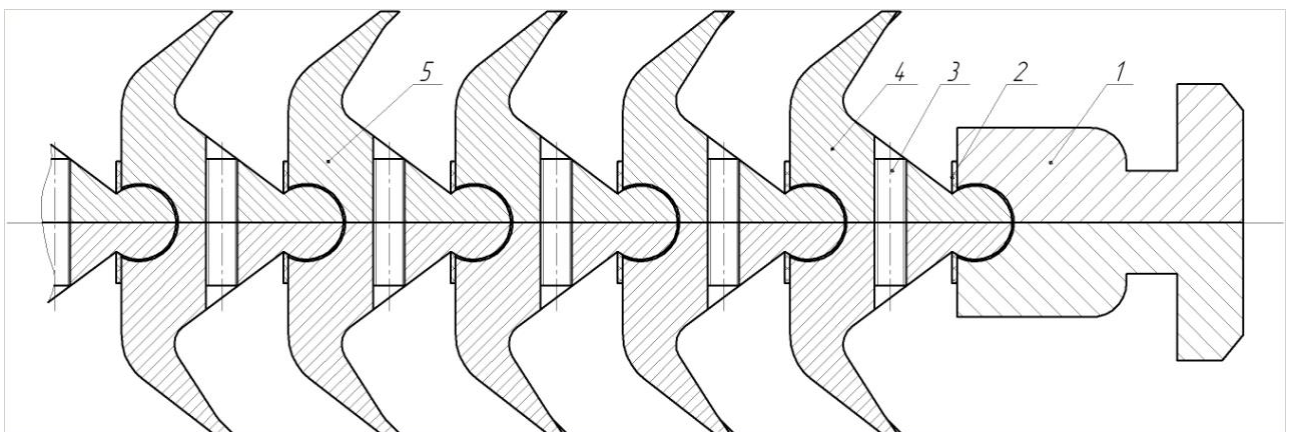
Конструкція гнучкої протяжки для оброблення отворів
